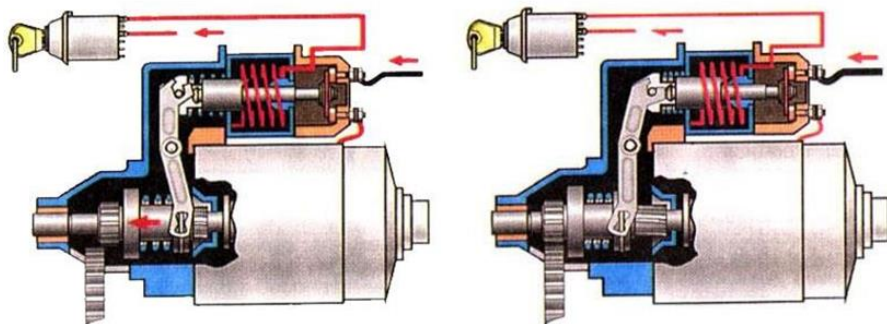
Зацепление шестерни привода с венцом маховика двигателя:
